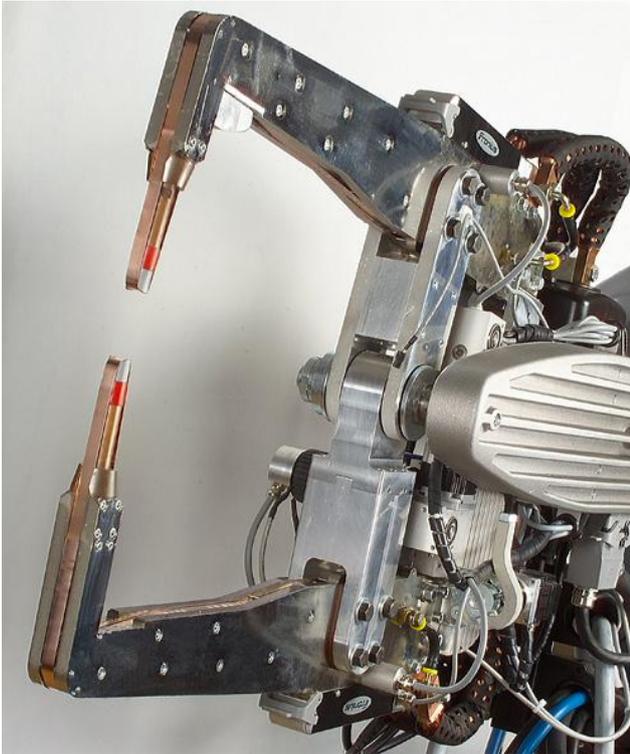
Сварочные клещи – новый процесс DeltaSpot для контактной сварки значительно увеличивает срок службы электродов, повышает качество и производительность сварки листовых конструкций.
